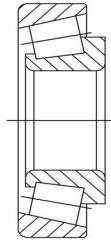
Роликовий підшипник радіально-упорний конічний.
